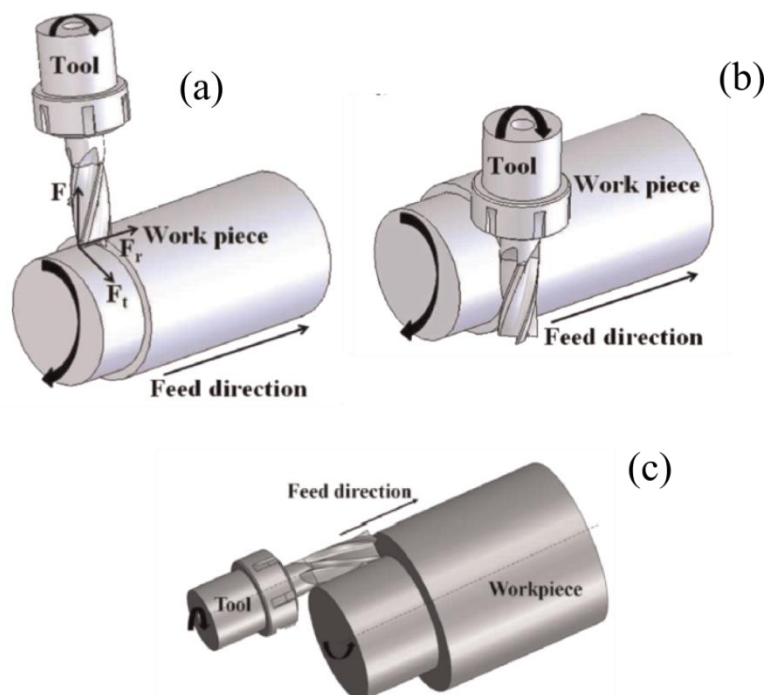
Géométrie de la coupe en tournage-fraisage combiné. Configuration de coupe : (a) orthogonale (b) tangentielle (c) coaxiale [Karagüzel et al, 2015].
